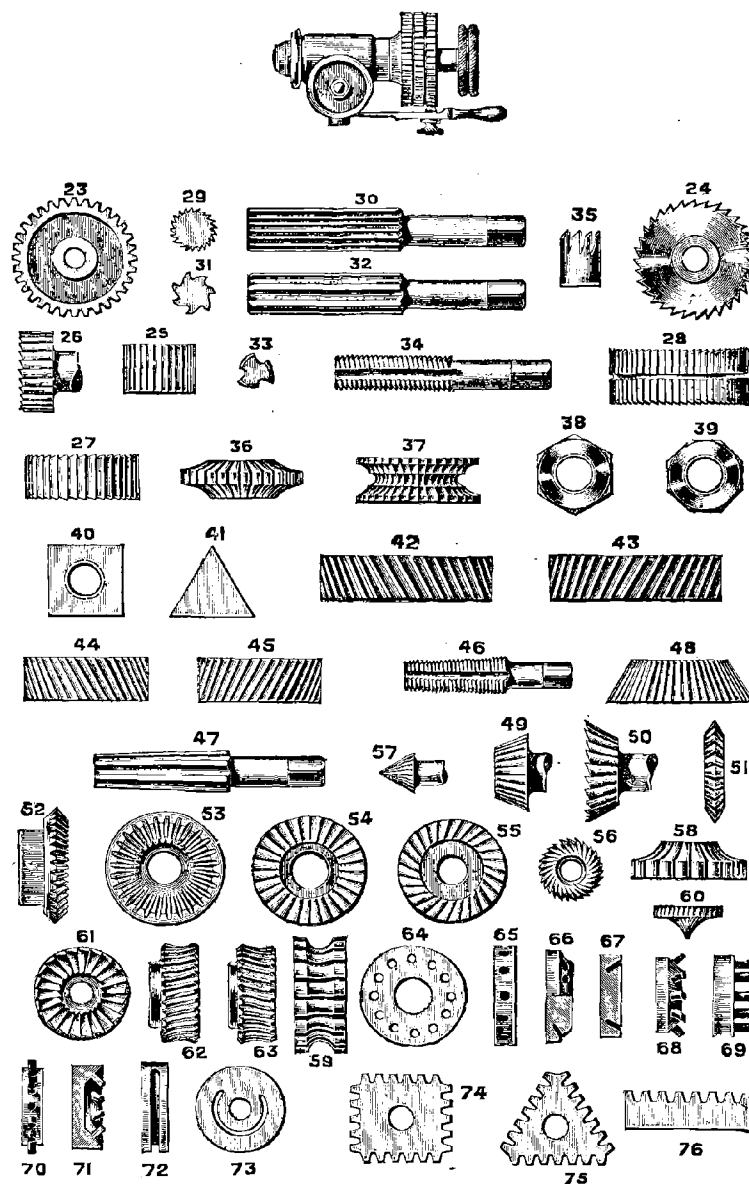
Quelques opérations de fraisage pouvant être exécutées avec la machine universelle à travailler les métaux.
